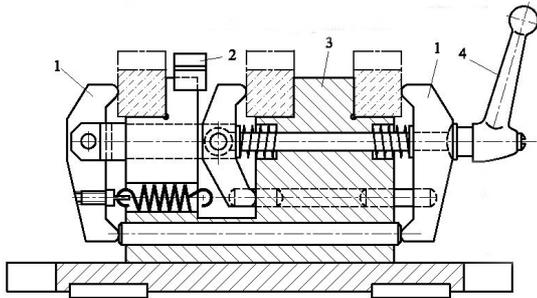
Fräsvorrichtung für drei Werkstücke
